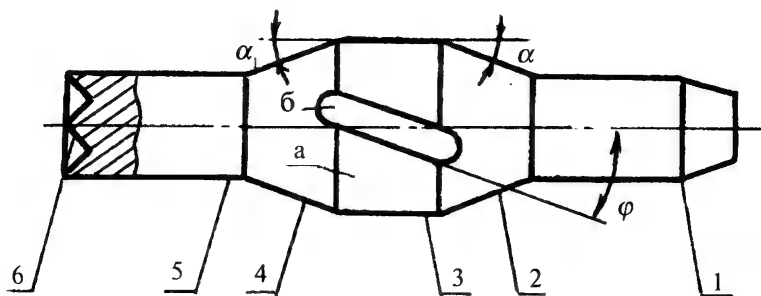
Конструкция дорна: 1 - направляющая часть, 2 - заходный (заборный) конус, 3 - калибрующая часть, 4 - задний конус, 5 - хвостовик, 6 - коническая пятка дорна; а - выступ, б - впадина
